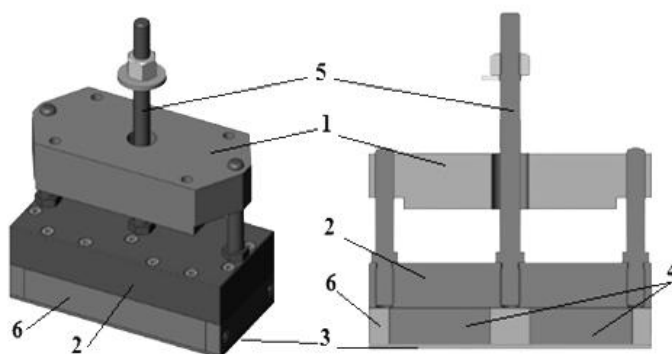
Фотореалистическое изображение блока постоянных магнитов; слева – 3D модель блока, справа – вид блока в разрезе: 1 – узел крепления, 2 – стальной магнитопровод, 3 – нижняя пластина корпуса ПМ, 4 – ПМ, 5 – шилька подвеса блока, 6 – корпус ПМ
